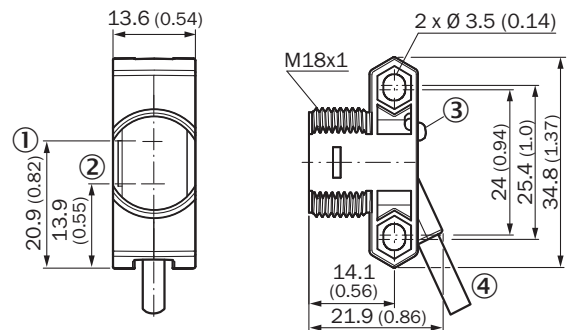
ZLx18-2xxxxx/ZLx18-Bxxxxx, cabo
